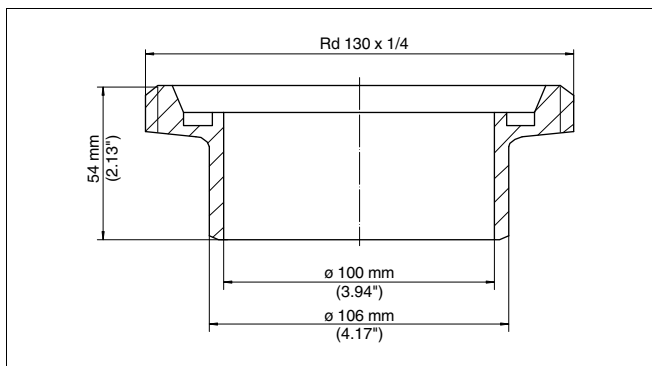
Размеры приварного штуцера - накидная гайка DN 100 по DIN 11851
